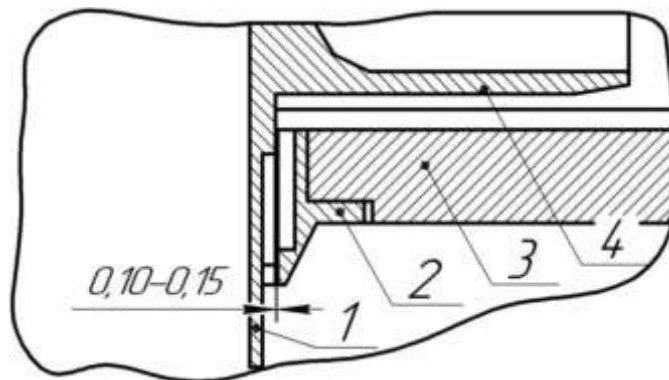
Промежуточная опора центробежного насоса: 1 – ступица рабочего колеса, наплавленная материалом ТМ1; 2 – уплотнительное кольцо, наплавленное ТМ1; 3 – направляющий аппарат; 4 – рабочее колесо
